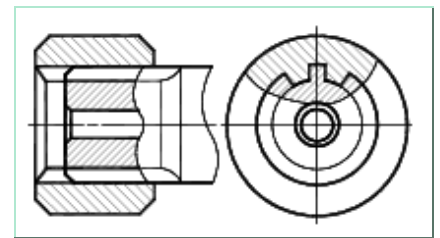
Условное изображение шлиц на чертеже [ГОСТ 2.409-74*]
